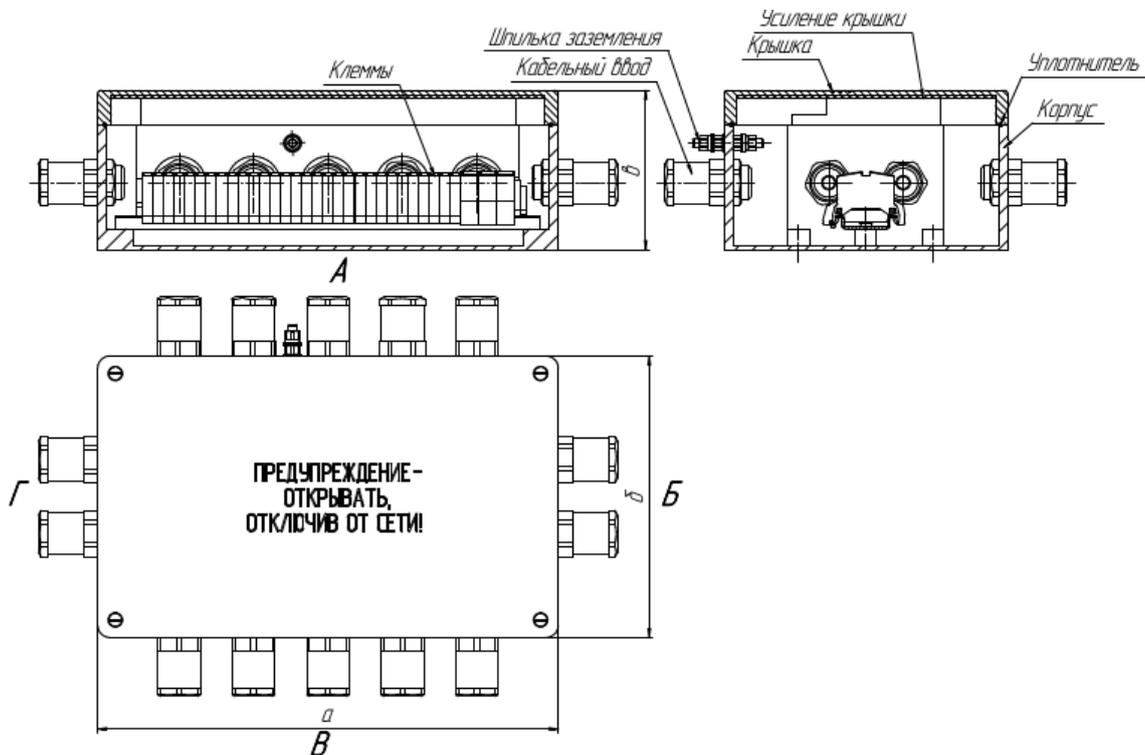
Общий вид , габаритные и присоединительные размеры коробок ЕхКК-А без сервисных компонентов
